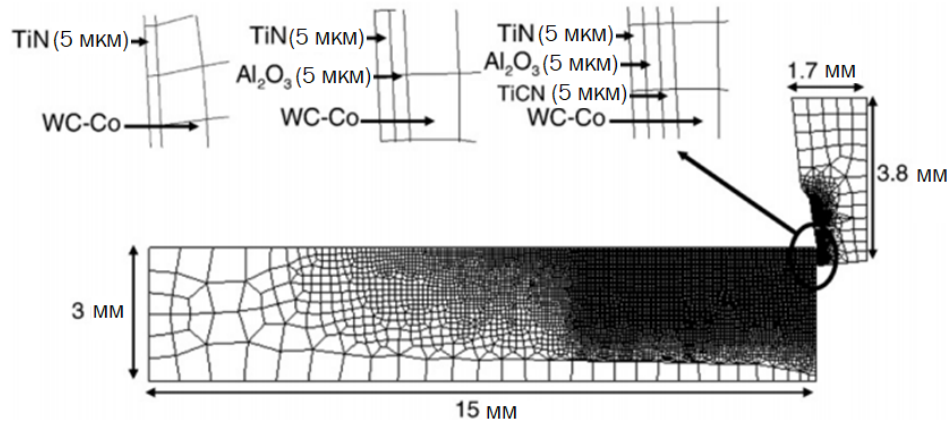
Геометрія, сітка та розміри заготовки, ріжучого інструменту та шарів покриття [99].
